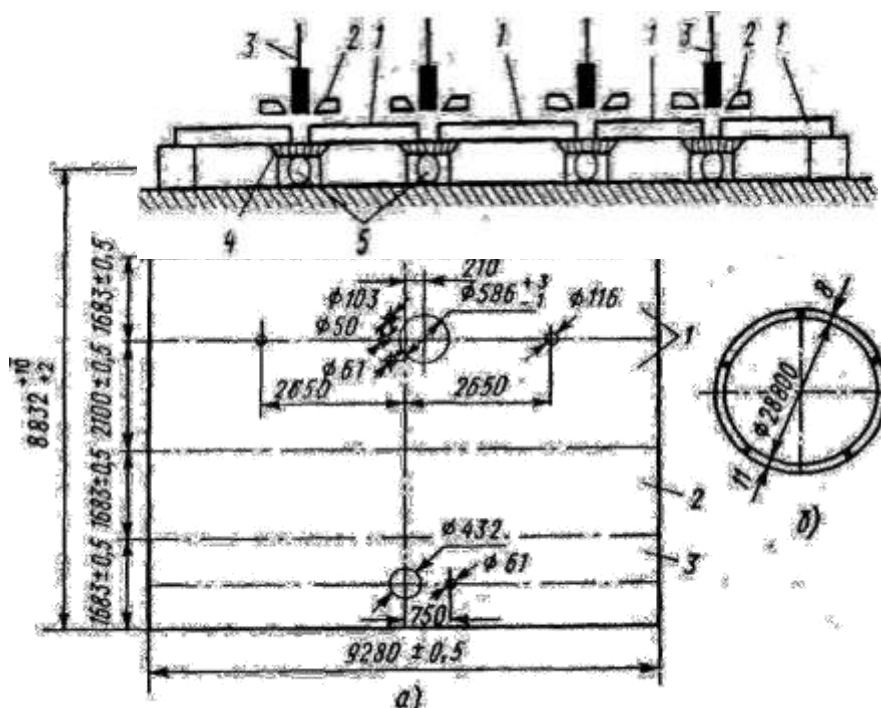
Схема стенда для автоматической сварки листов обечайки
